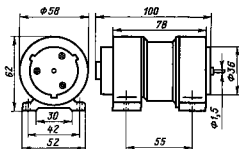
19 Габаритные и установочные размеры двигатель-генератора ПТП-5
